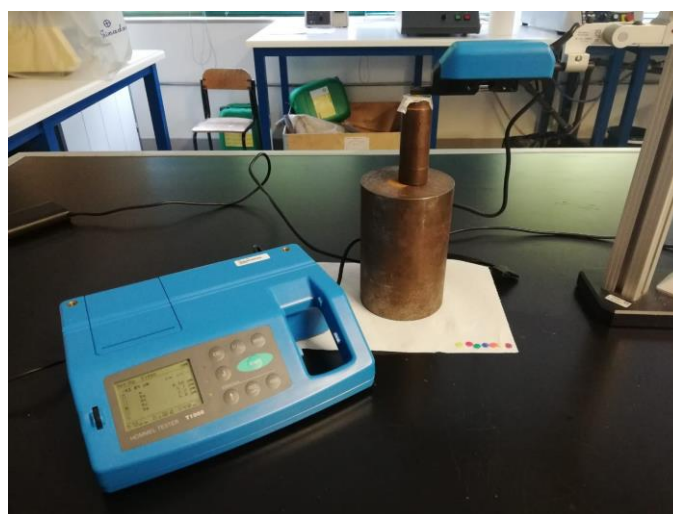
Medição do disco Gold com Hommel Tester T1000[®].
